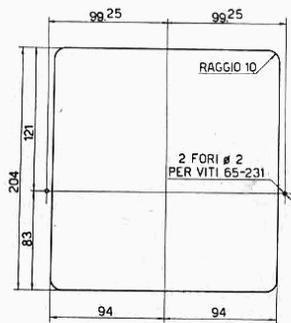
Piano di foratura per montaggio in mobile del diffusore
